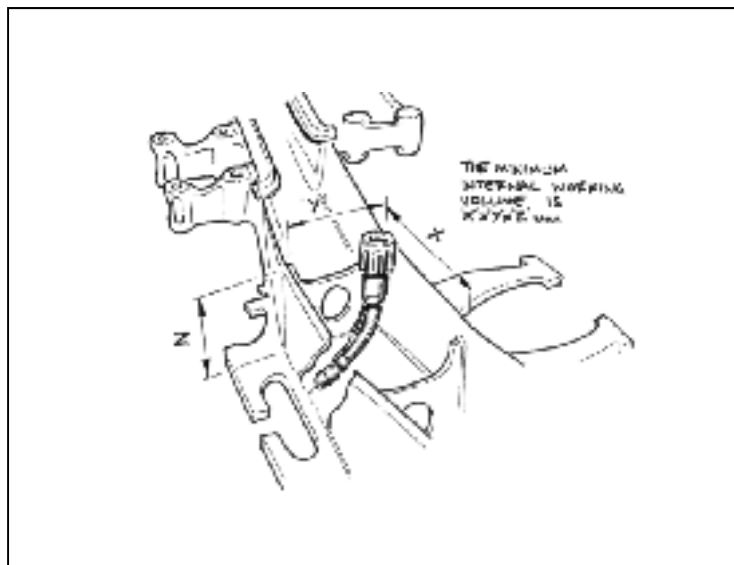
Croquis de vérification d'accès à la soudure
